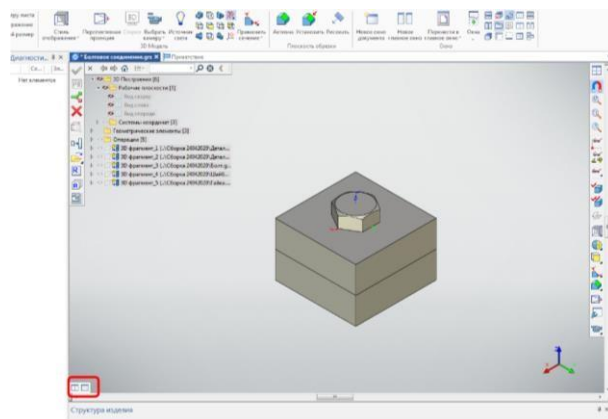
Сборка перед созданием сборочного чертежа (сборочной 2D модели)
